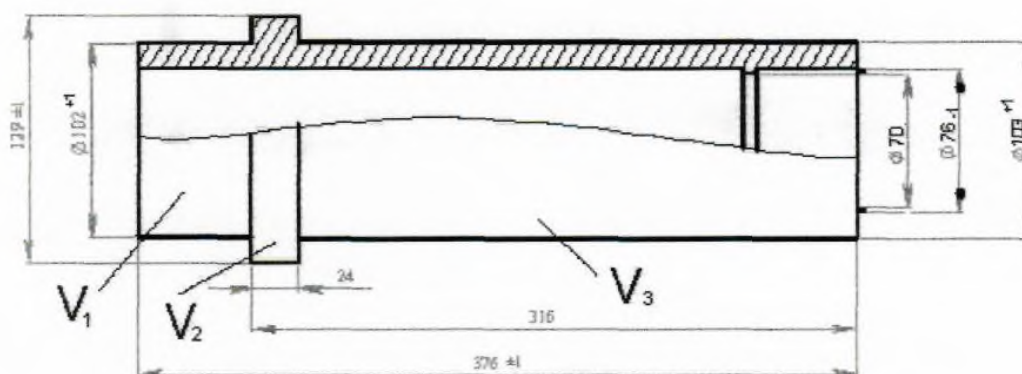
Схема розбиття заготовки на елементарні обсяги
